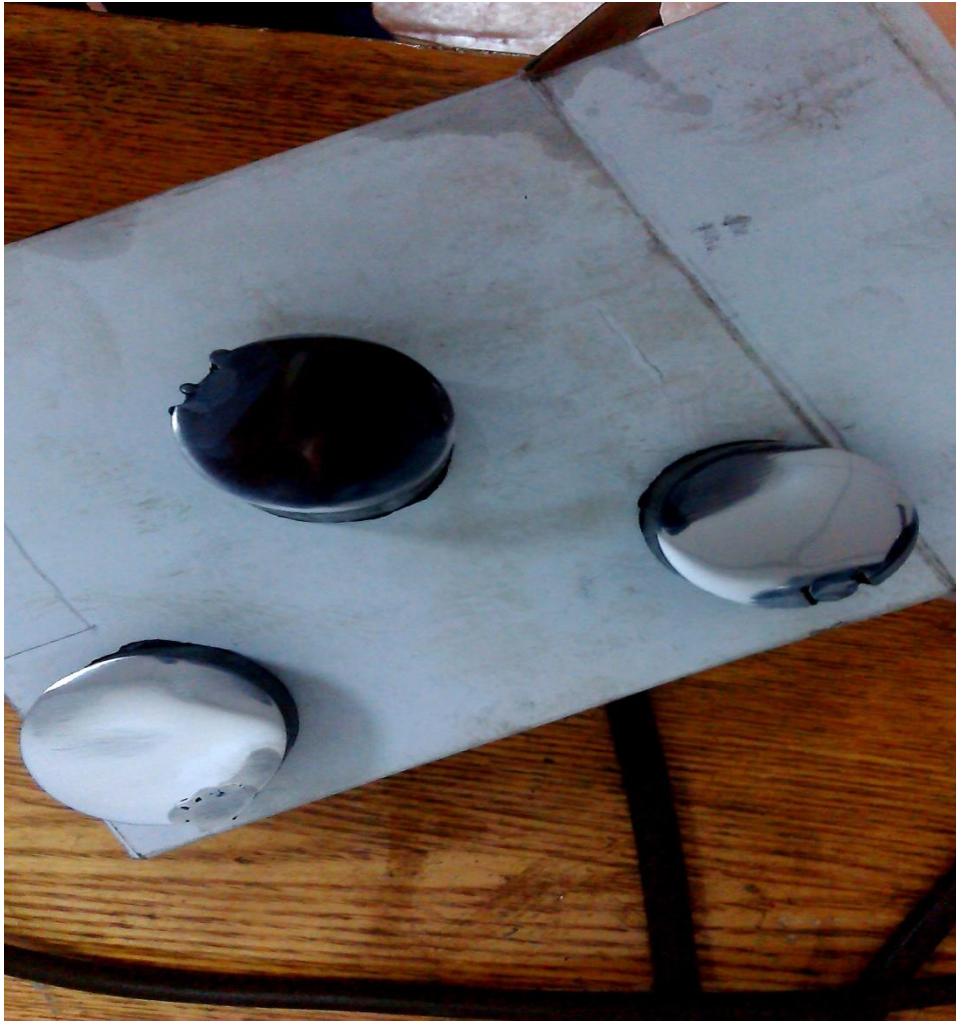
Напилені зразки з використанням металізатора EM-14 M
